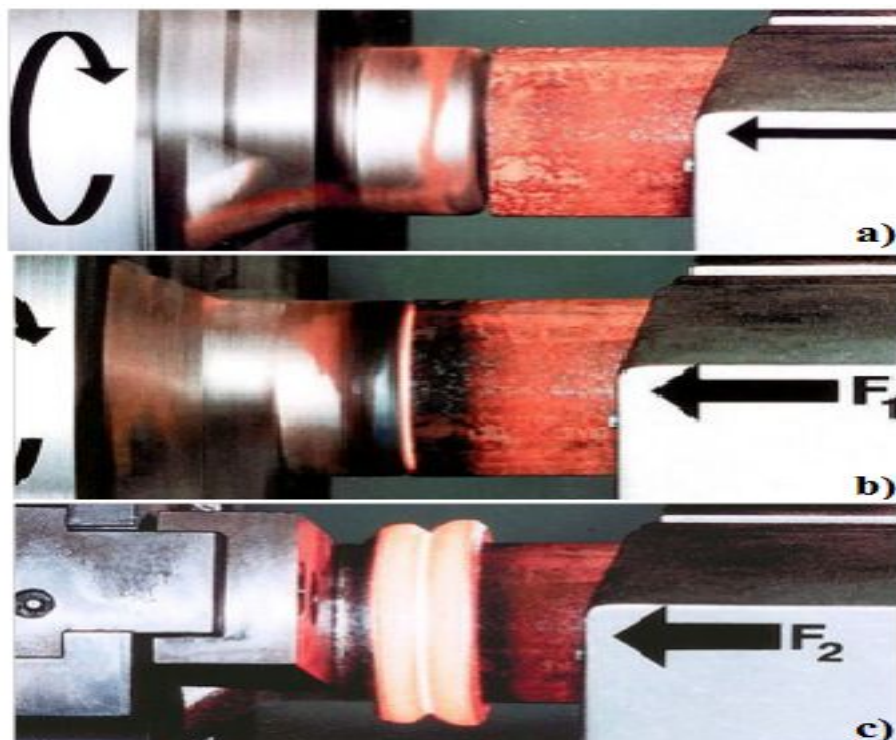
principe de soudage par friction ; a) Les deux pièces sont clamées et une des pièces est mise en rotation, b) Les pièces sont mises en contact l'une de l'autre avec la force de friction  $F_1$ : la température augmente dans la surface de contact, c) La partie en rotation est freinée et la force de forgeage  $F_2$  est exercée [16].
